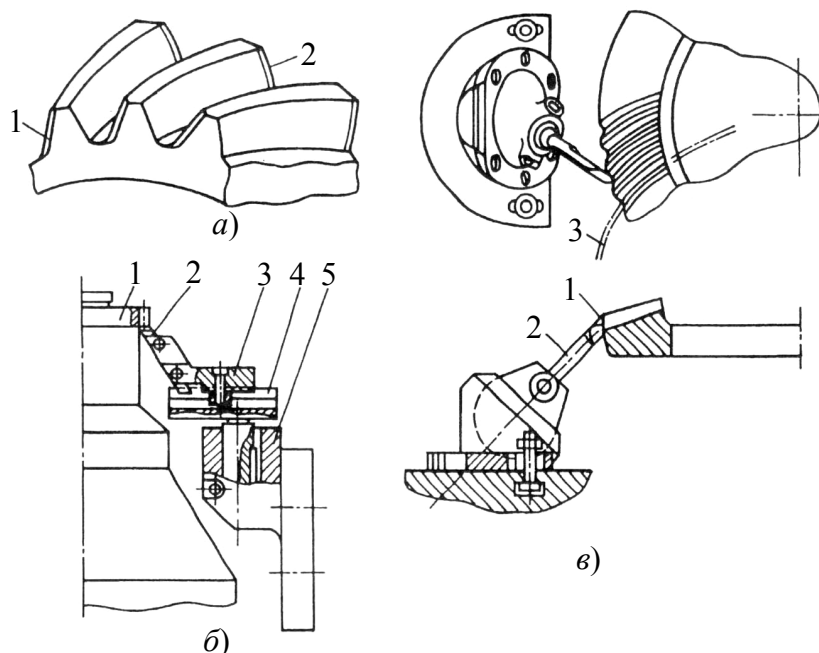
Схема снятия фасок острых кромок зубьев (а) и удаление заусенцев (б, в): 1 – обрабатываемое колесо; 2 – резец; 3 – державка; 4 – направляющая; 5 – корпус приспособления
